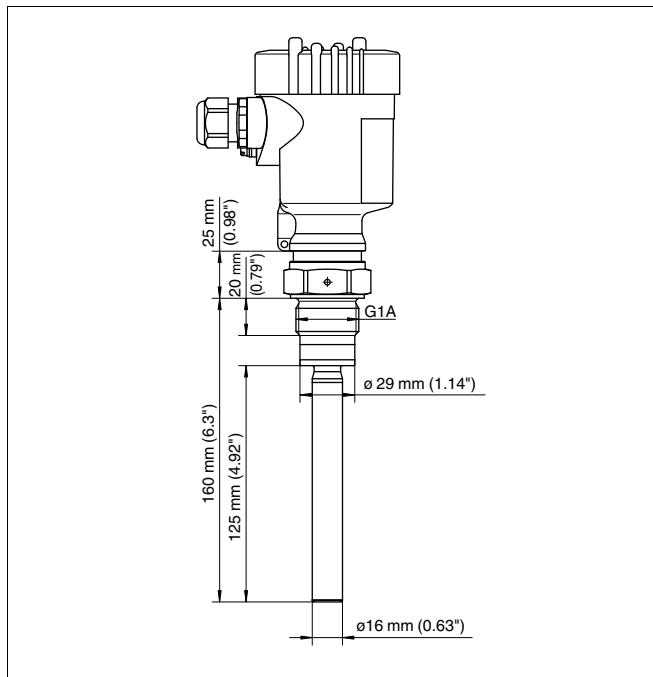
VEGA VIB 61, резьбовое исполнение G1 A (DIN ISO 228/1)
